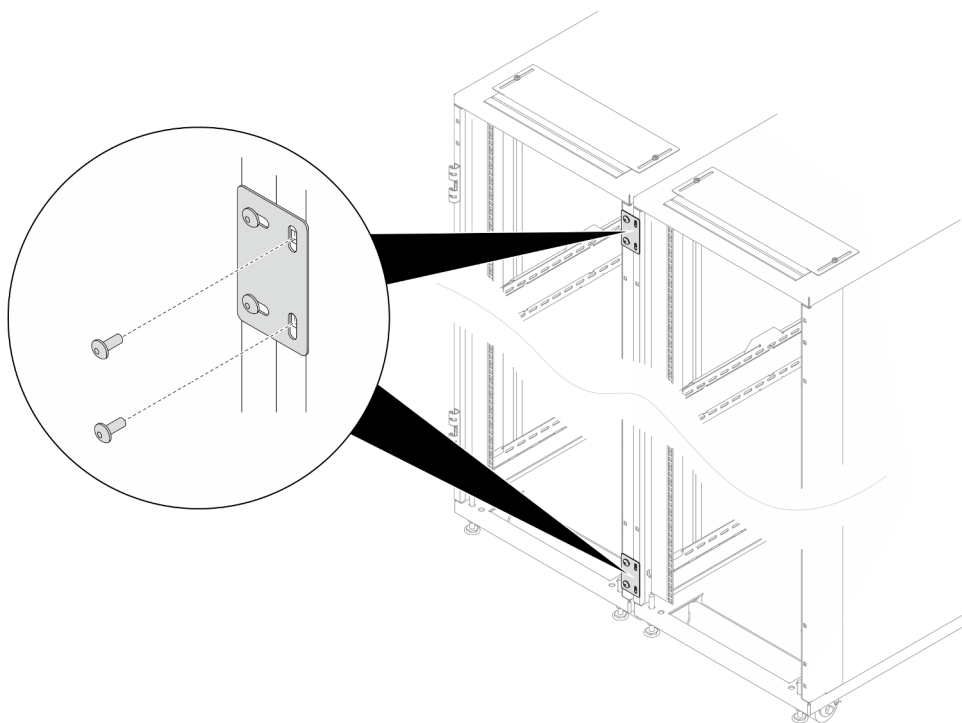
Rimozione delle viti per preparare l'installazione dell'estensione
